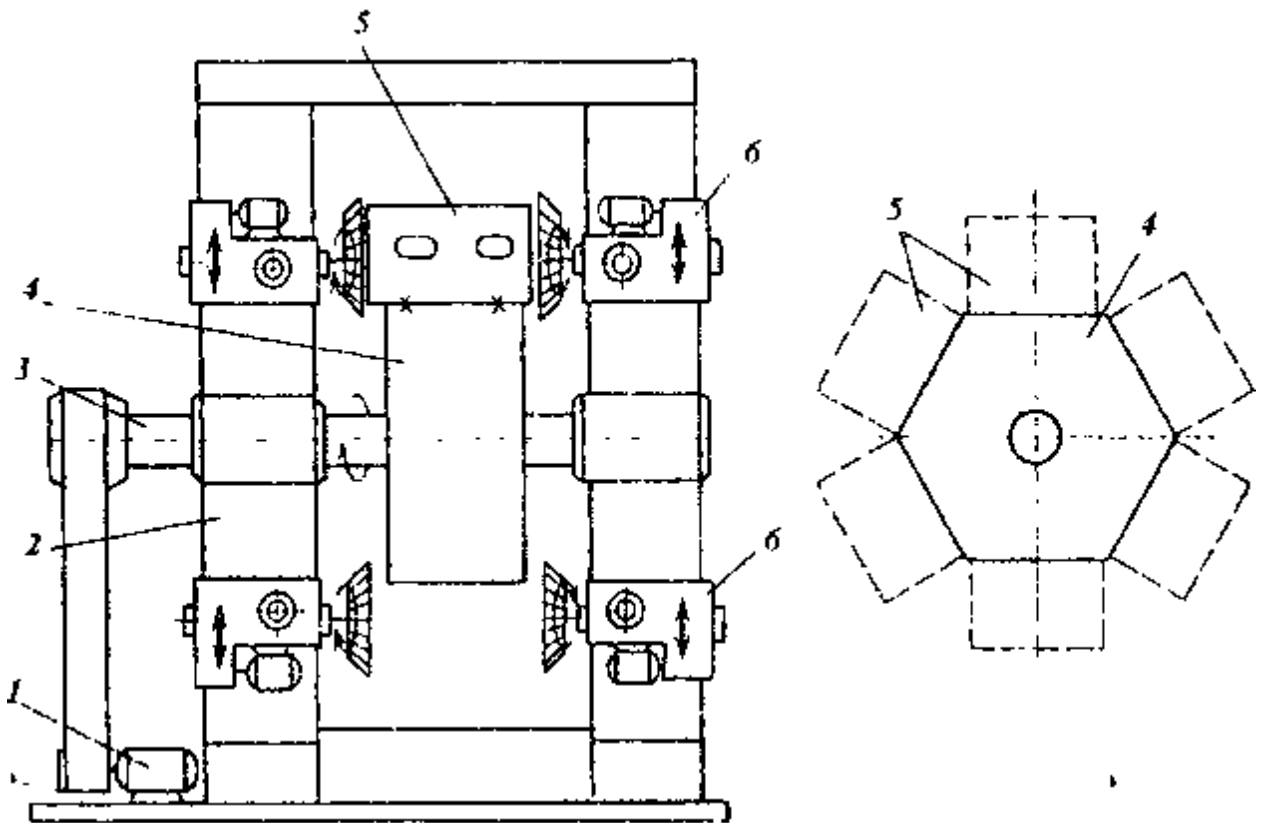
Схема обробки деталей на барабанно-фрезерному верстаті
